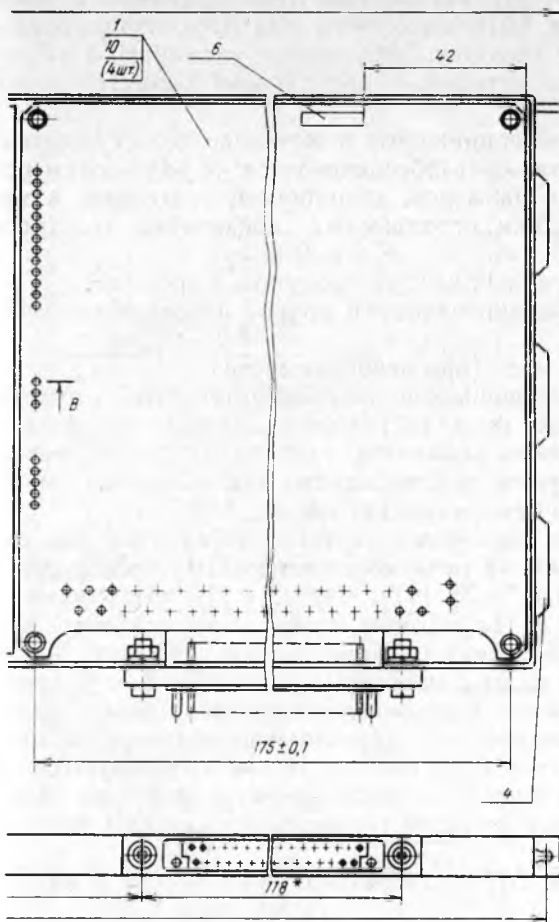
Сборочный чертёж ячейки блока ВКЦ
